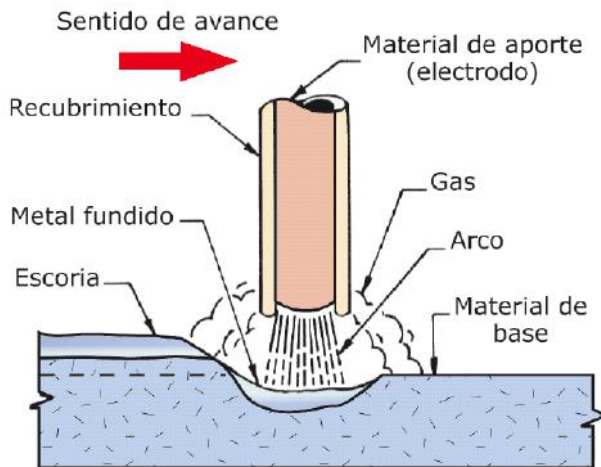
Proceso de soldadura, tomada de Rodríguez P.C. (2001).
